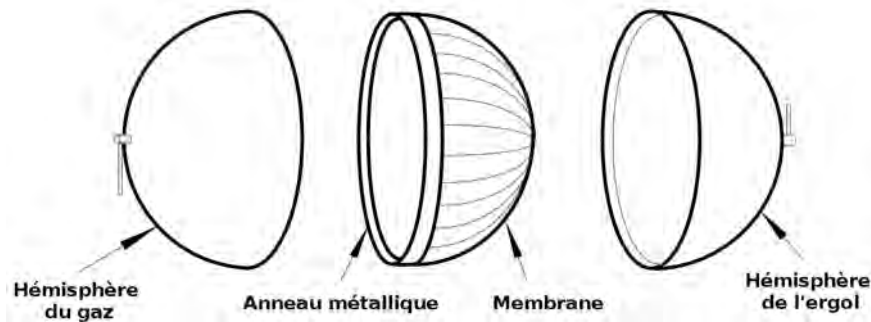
Vue éclatée d'un réservoir à membrane [2].
